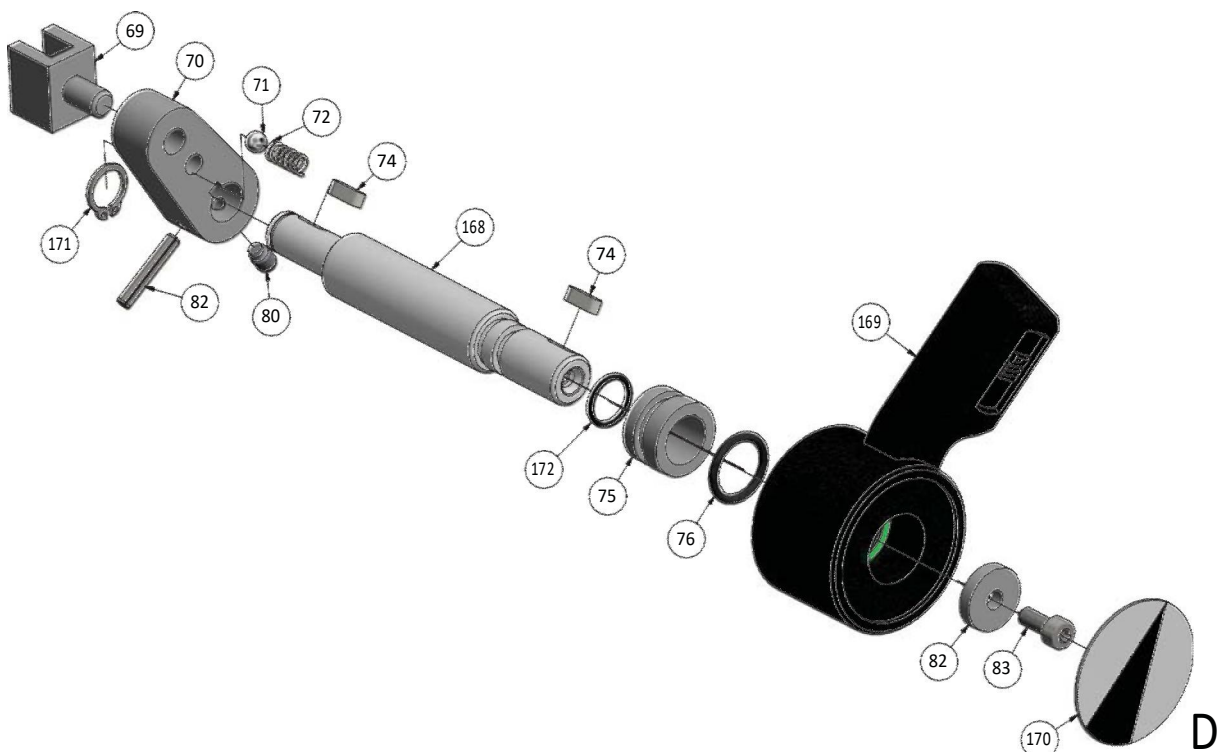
Vorschubgetriebe 6-9 –Engranaje de avance 6-9
